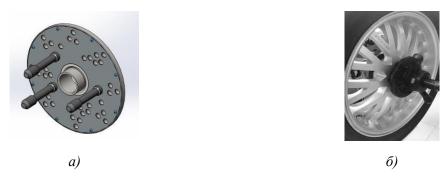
a) — Фланцевый адаптер; б) — Установка колеса с помощью фланцевого адаптера
